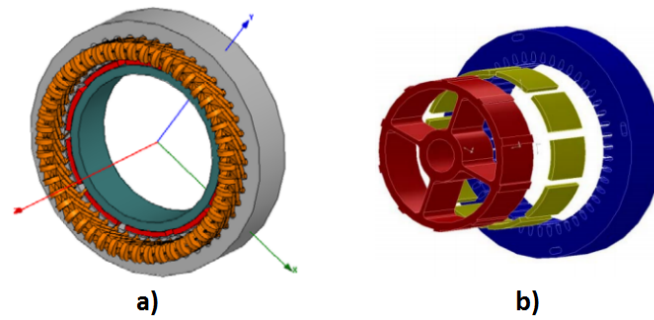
Gerador de ímãs permanentes de fluxo radial com rotor interno. a) Vista Compacta, b) Vista Explodida.
